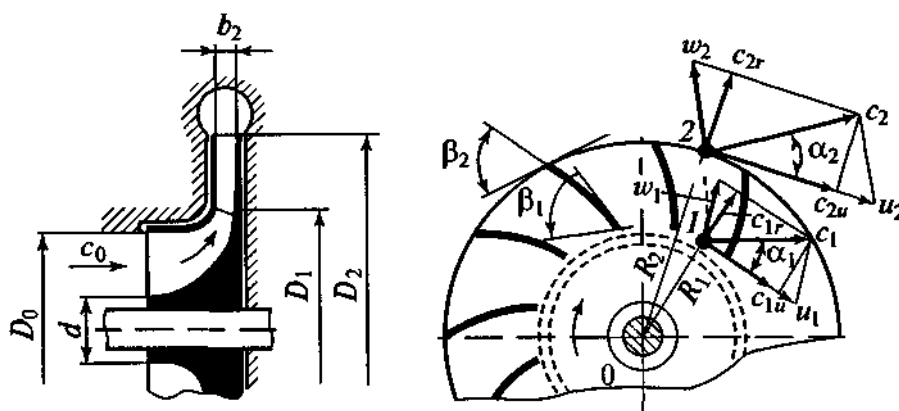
Схематическое изображение рабочего колеса центробежного нагнетателя
